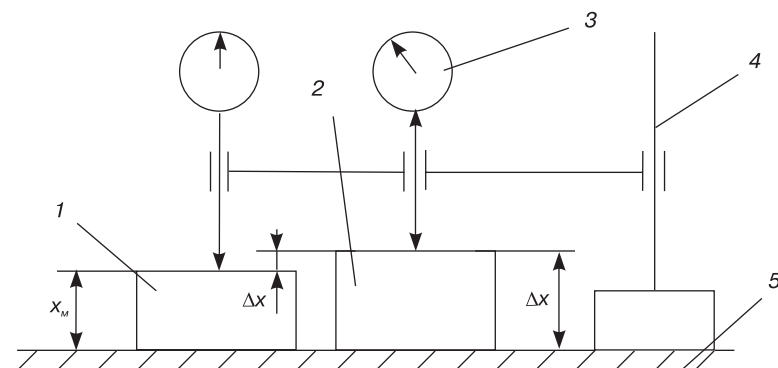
Схема измерения линейного размера детали дифференциальным методом (сравнением с мерой): 1 — блок концевых мер длины; 2 — измеряемая деталь; 3 — измерительная головка; 4 — штатив; 5 — поверочная плита
